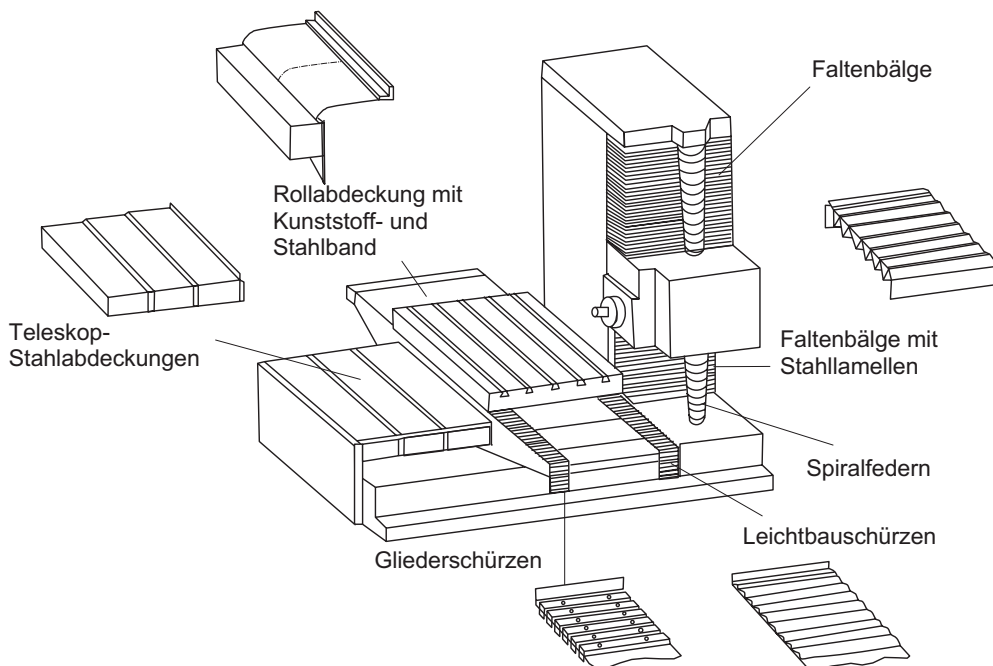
Abdeckung von Führungselementen in Werkzeugmaschinen. Quelle: Hennig
